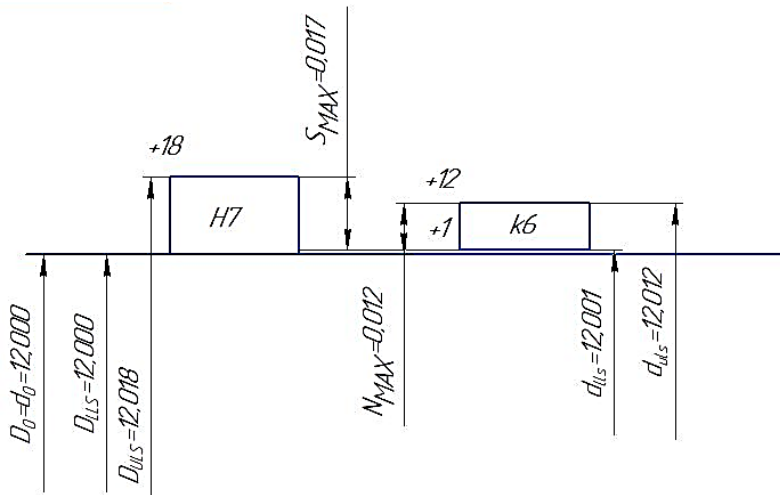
Схема расположения полей допусков вала и отверстия
